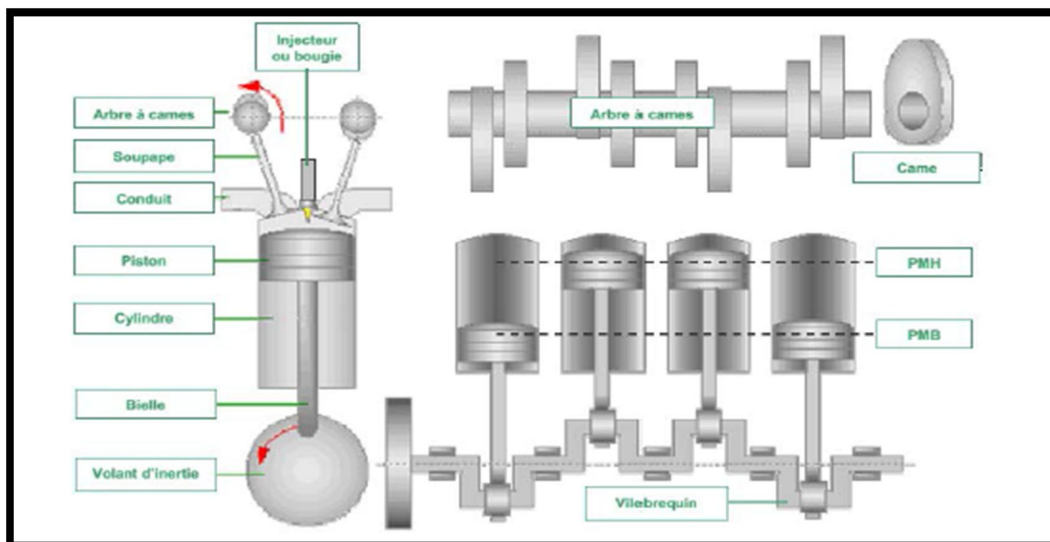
Composants principaux d'un moteur alternatif à pistons [22].
